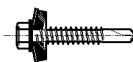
BOHRSCHRAUBE  $\varnothing = 5,5 \text{ mm}$
